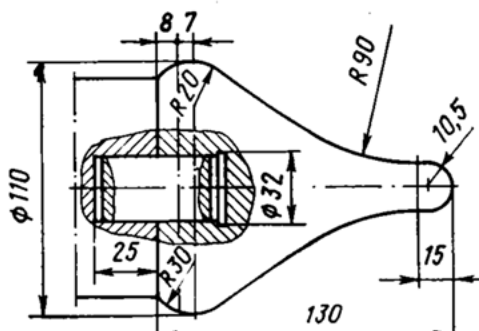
Оправка для експандування свердлених гільз, [9]
